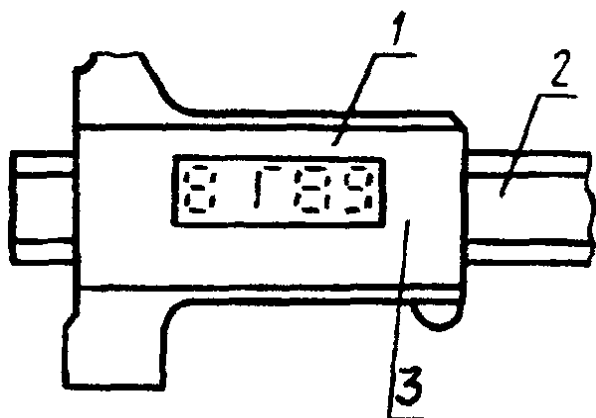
1- цифрова шкала відлікового пристрою; 2- штанга; 3- рамка;
